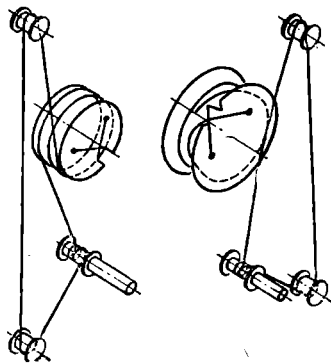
Кинематическая схема верньерного устройства радиоприемника «Ленинград-002»
